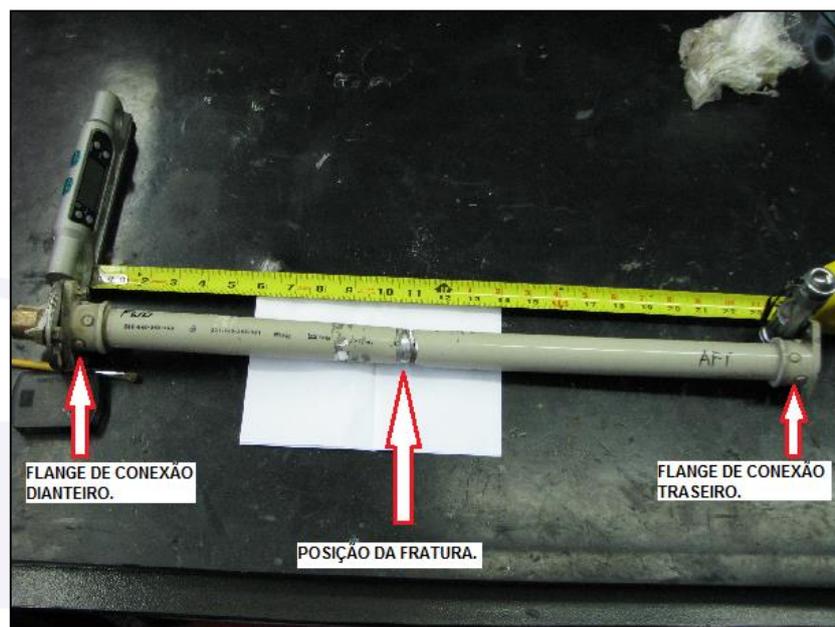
Posição da fratura da 1ª parte do eixo segmentado a 11 polegadas do flange de conexão dianteiro.
